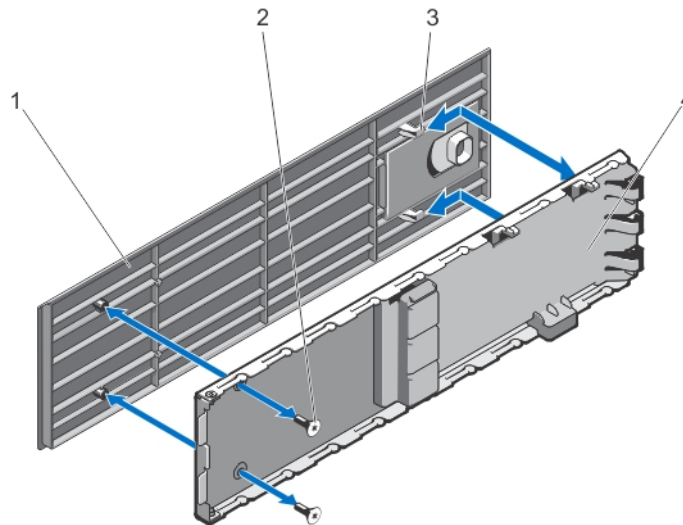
Entfernen und Installieren der PCIe-Gehäusetürabdeckung
